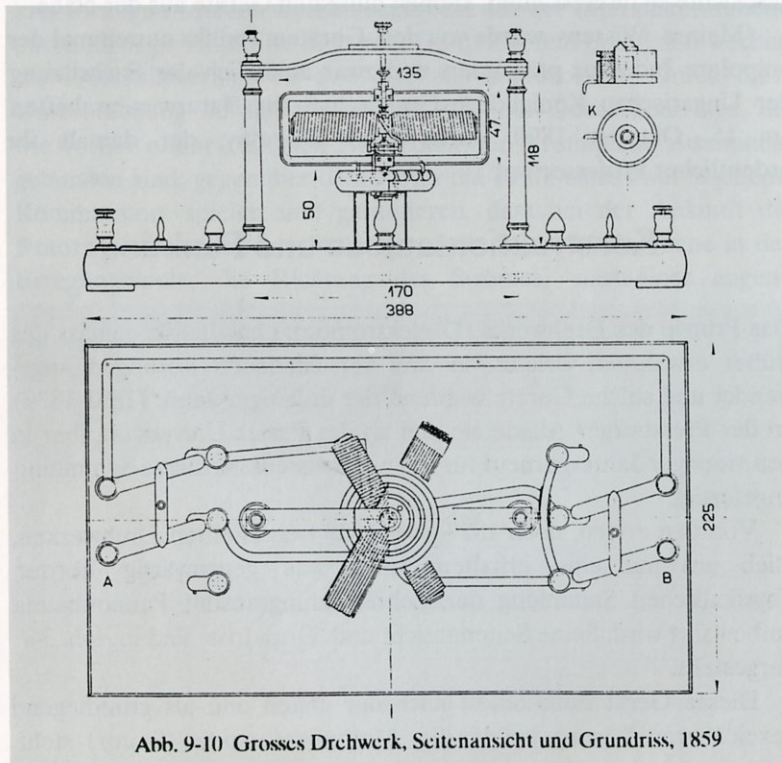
Grosses Drehwerk, Seitenansicht und Grundriss, 1859
